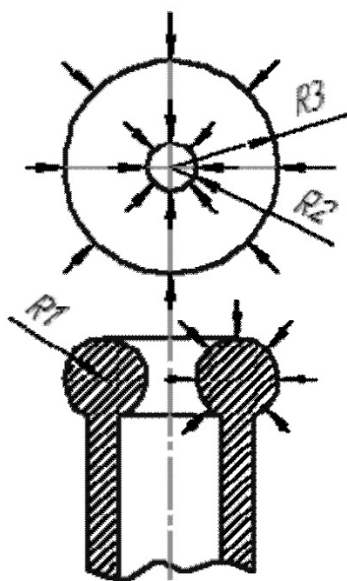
Действие сил поверхностного натяжения на расплавленный торец
